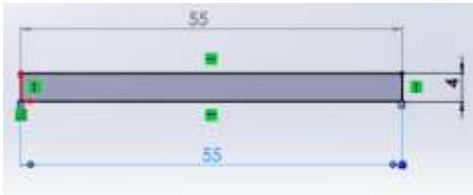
2Dimensi Hollow stainless steel 65 cm
